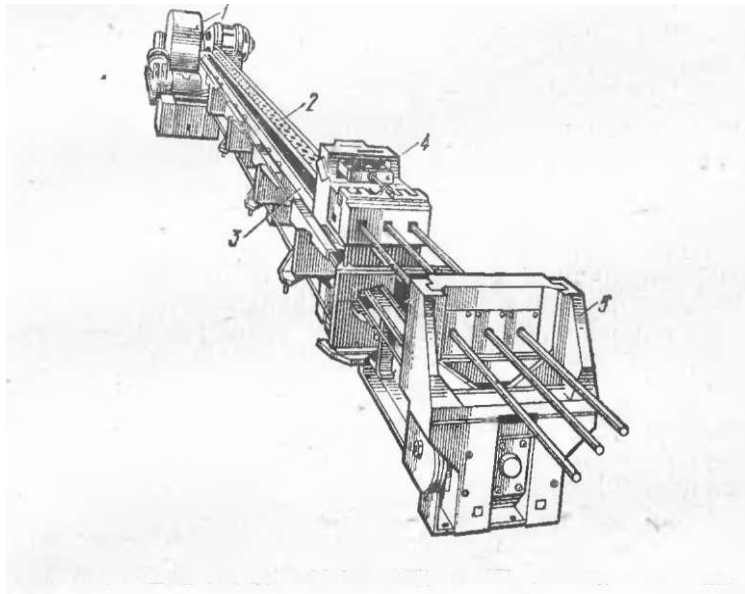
Общий вид цепного многопруткового волочильного стана
